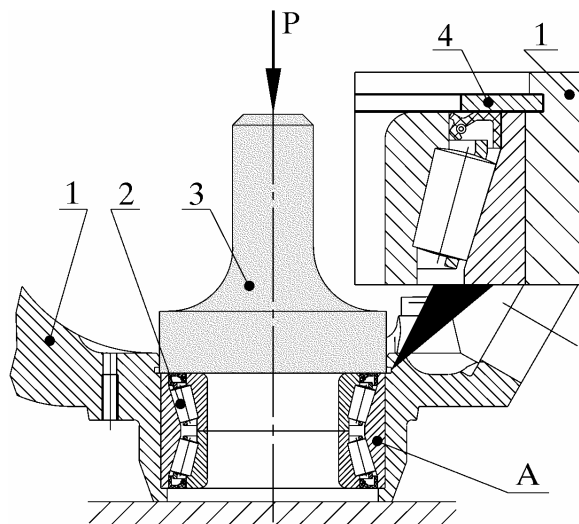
Запрессовка подшипника в отверстие поворотной стойки левой (правой) и установка стопорного кольца подшипника:
